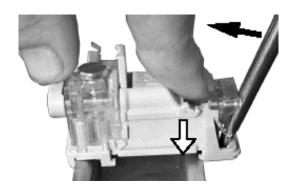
Установка соединителя МХ 2000 на монтажный профиль
